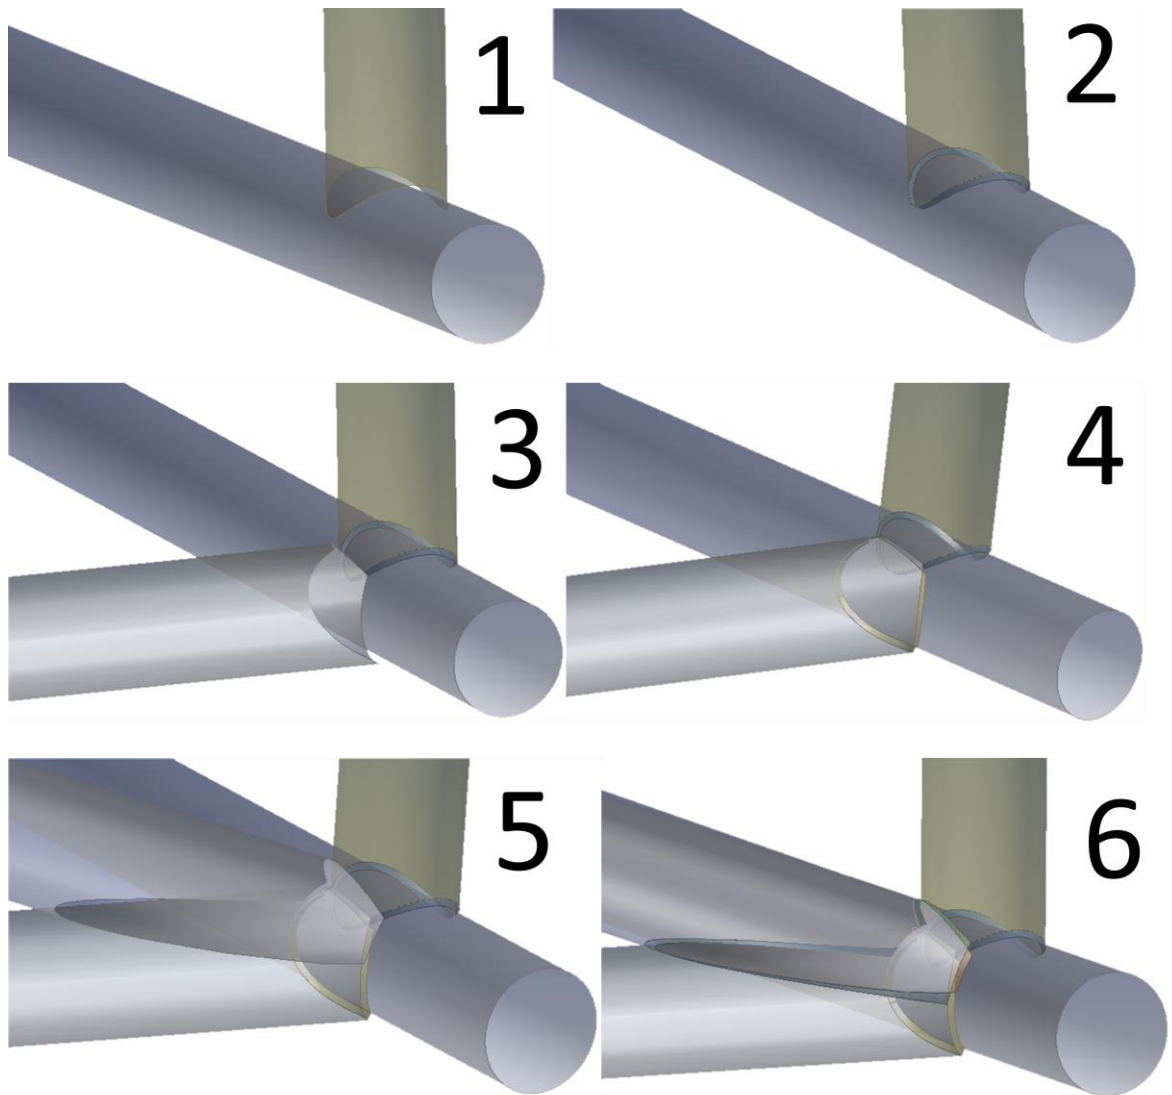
Processo de criação da soldadura numa ligação com vários tubos
